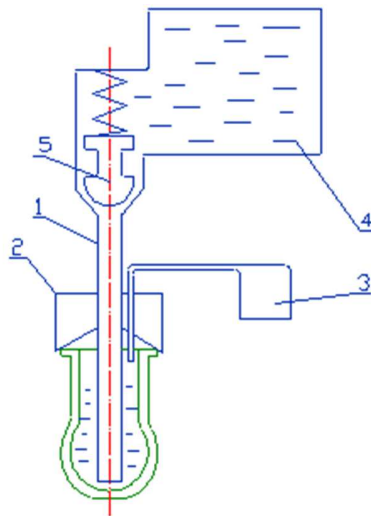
Схема двокамерного фасувального пристрою: 1 – зливна трубка; 2 – дзвіночок; 3 – газова камера; 4 – рідинний резервуар; 5 – клапан
